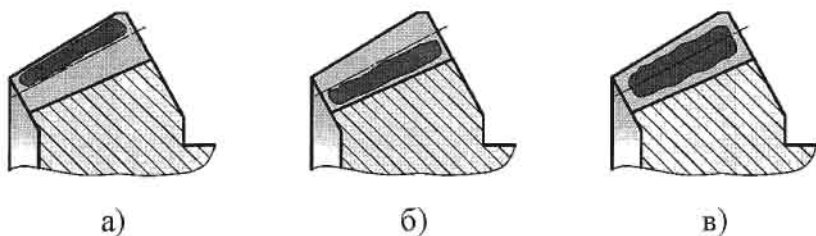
Расположение пятна контакта на зубе шестерни
